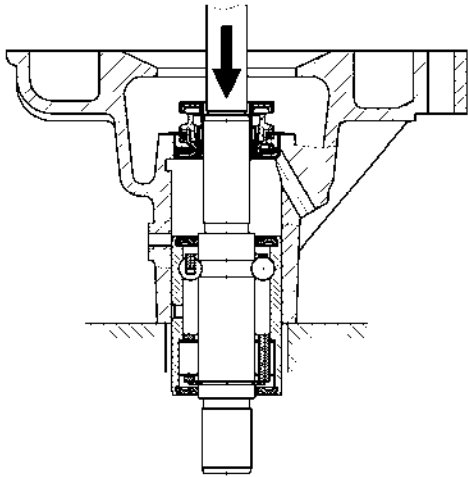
Lager auspressen mit Rollenwasserpumpe
